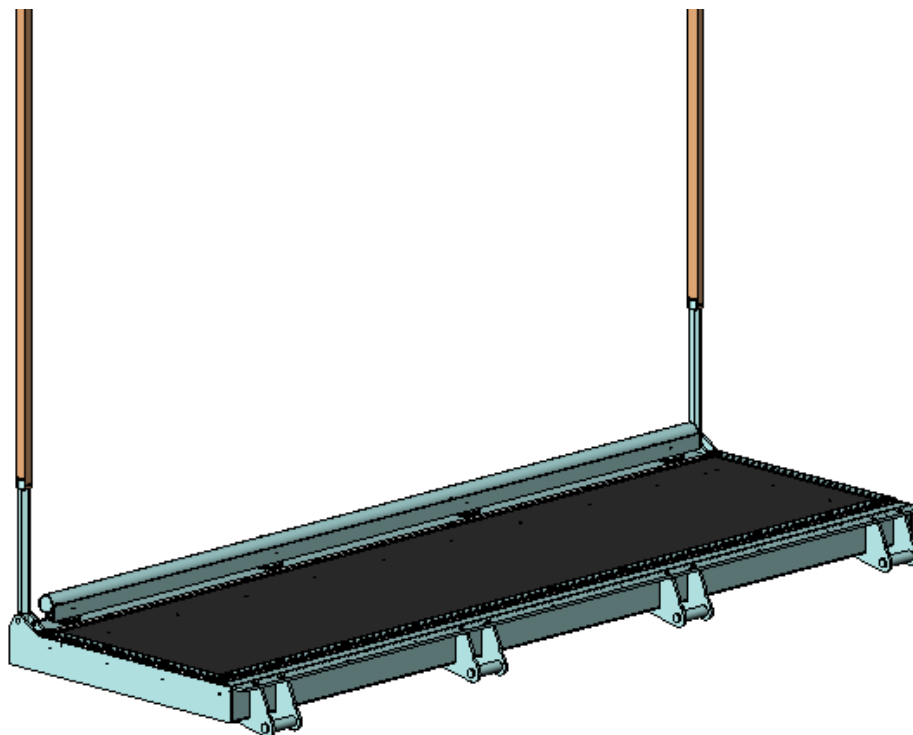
Подвижный пол бокса, соединенный с выпадающей дверью
